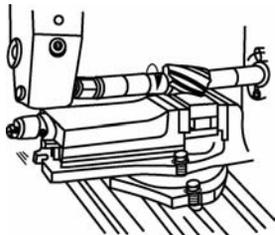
在卧式铣床上用圆柱铣刀铣平面
